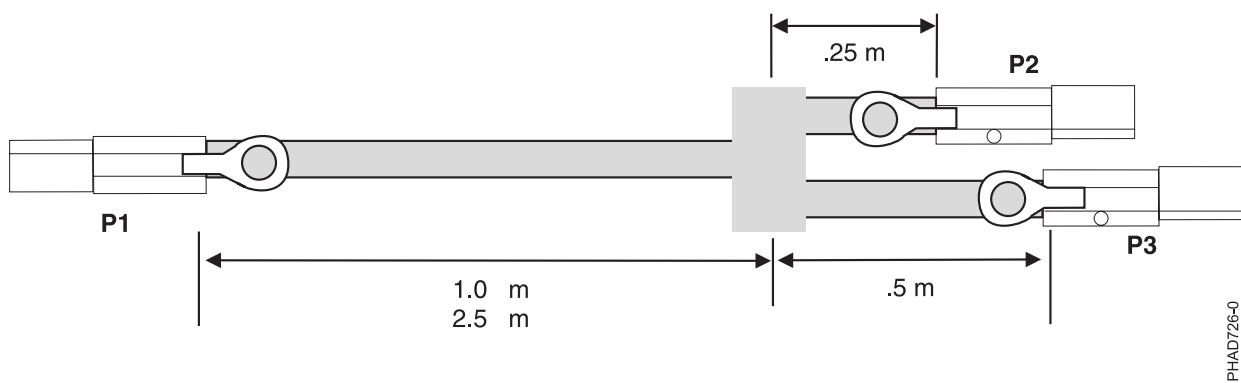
Comprimentos de cabo de montagem de cabo YI externo SAS
